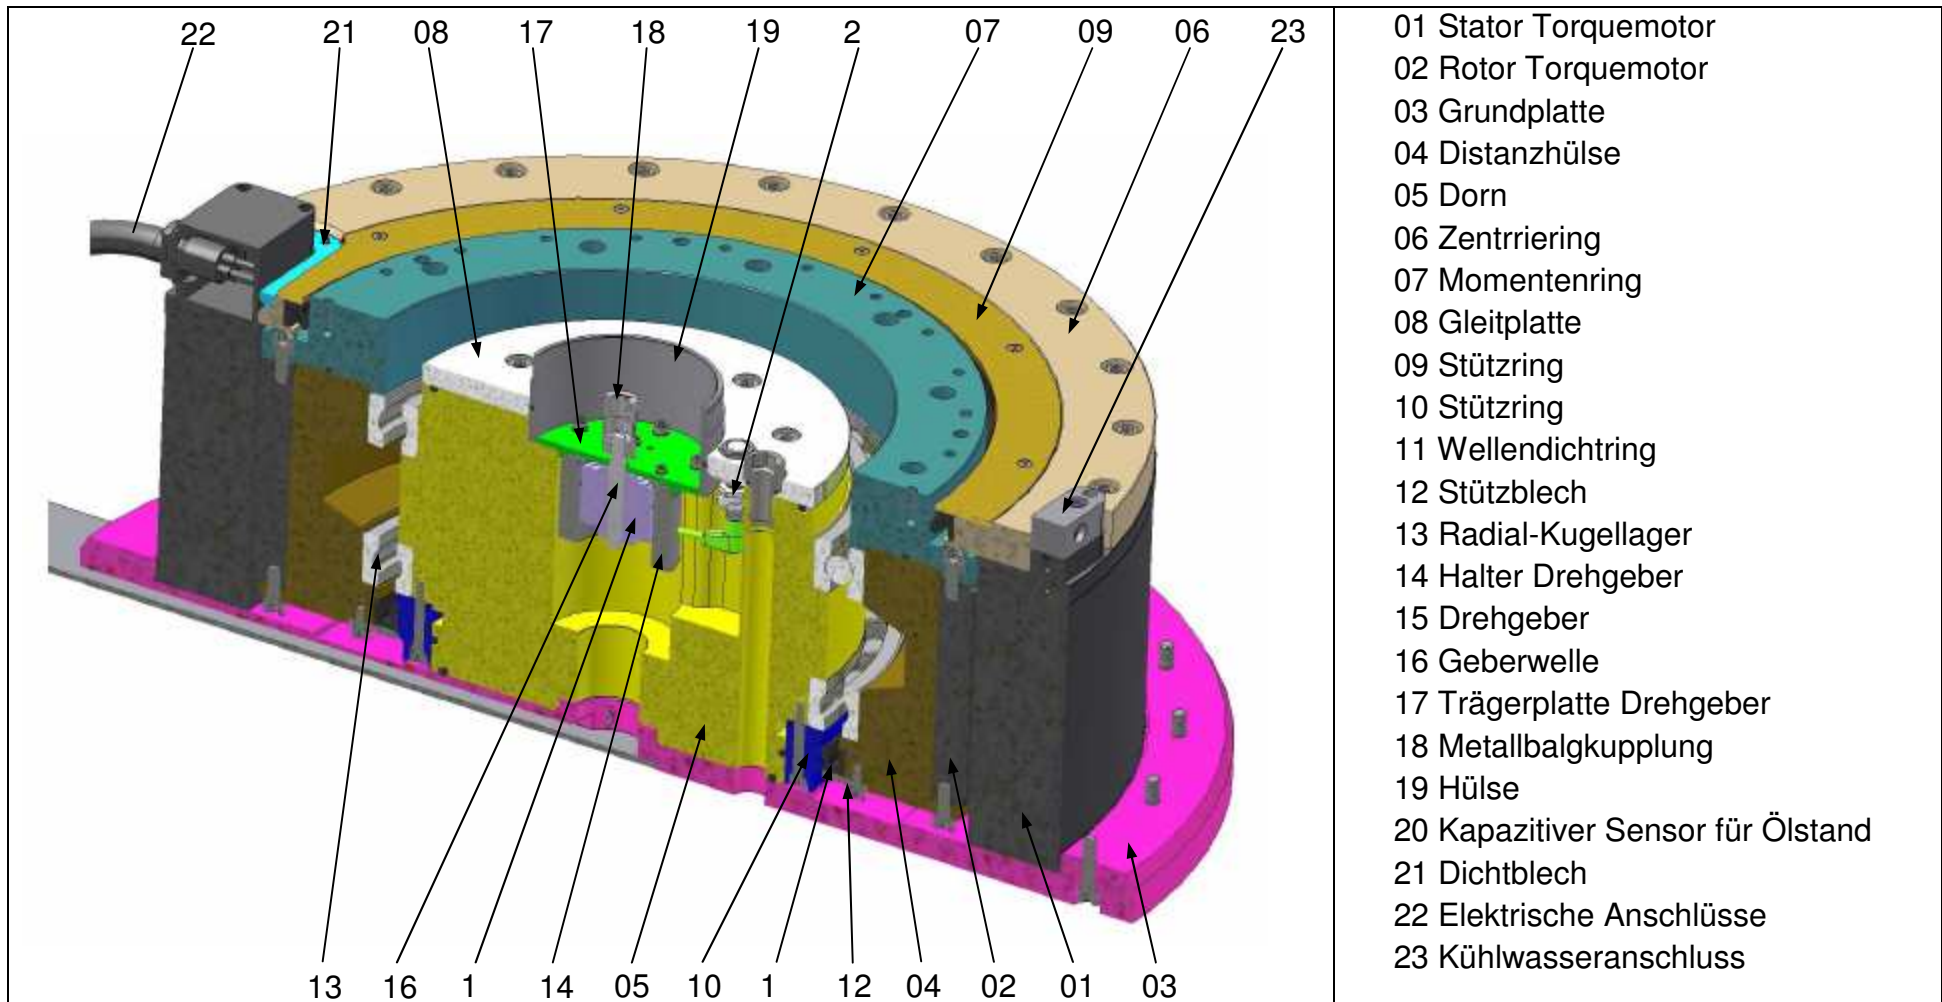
Schwenkantrieb mit Einbau-Torquemotor (bisherige Ausführung)
